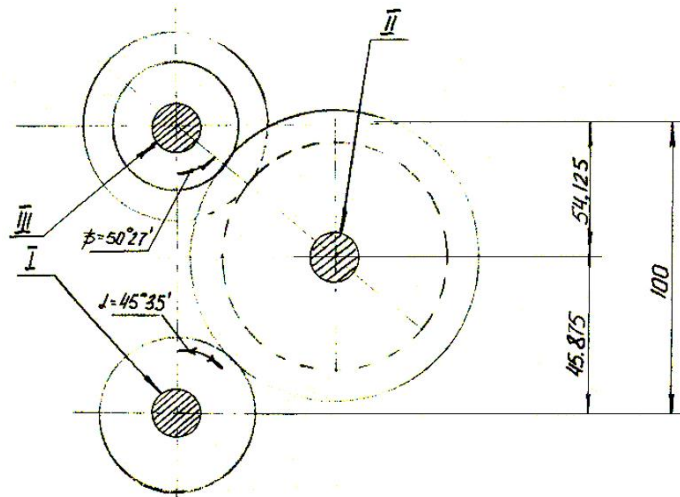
Поперечна компоновка коробки швидкостей верстату СФ80
